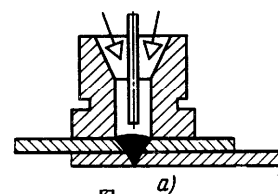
Насадки на сопло для дуговой точечной сварки
